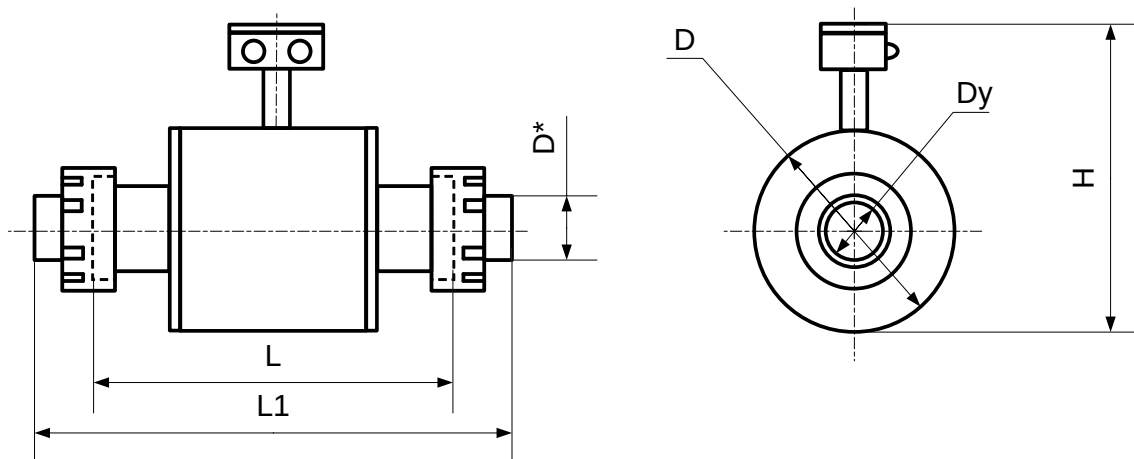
Габаритные, присоединительные размеры и масса резьбовых первичных преобразователей с метрической резьбой Рм, давление измеряемой среды PN до 16 МПа (до 160 bar) с клеммной коробкой и с разъемом
